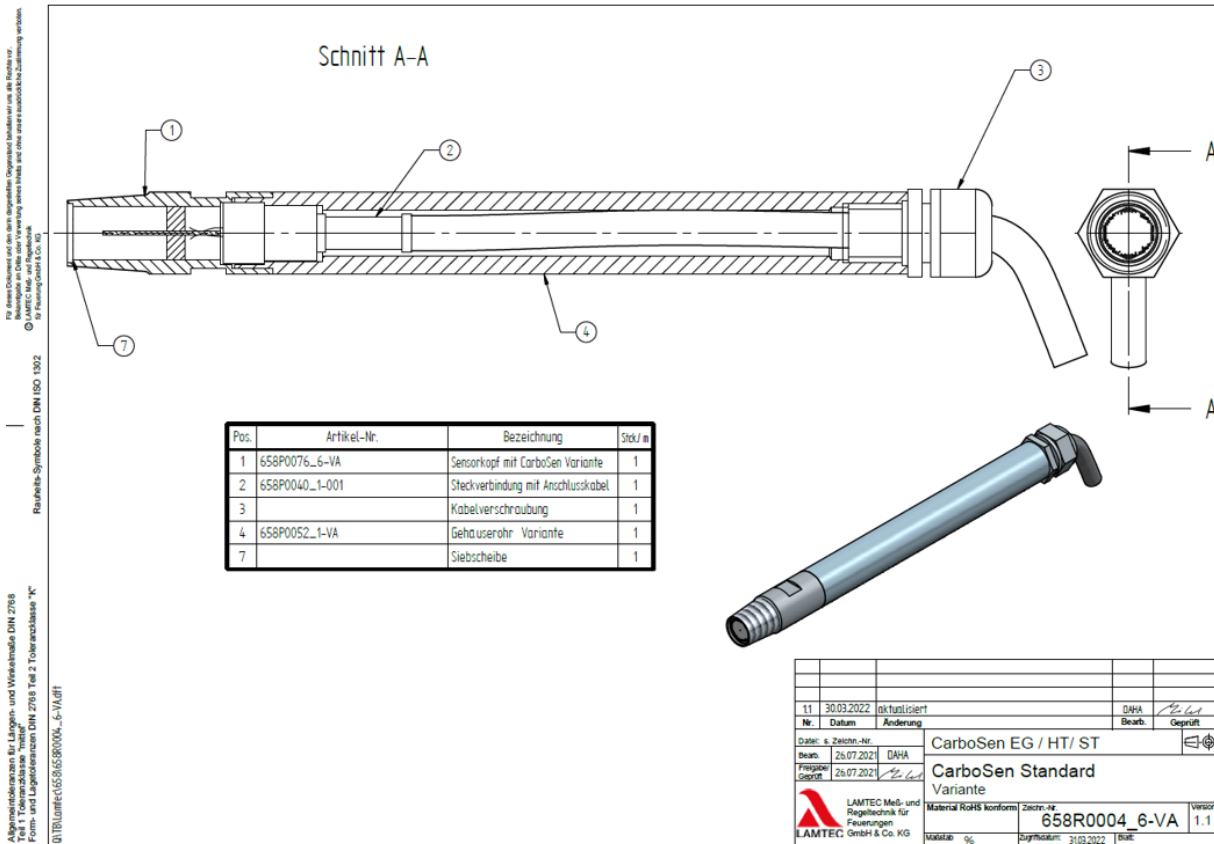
Gehäusekonzept der CarboSen-Sensorintegration mit neuer Sensor-Durchführung (hier lange Gehäuseversion)
